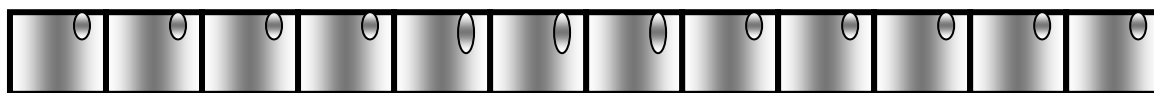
Схема контактных пятен зубьев ведущей шестерни редуктора
